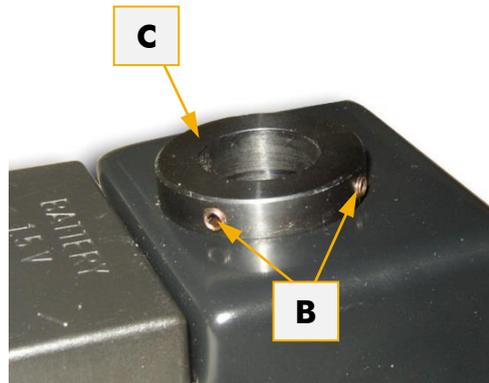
Hohlwellenkörper mit Madenschrauben
